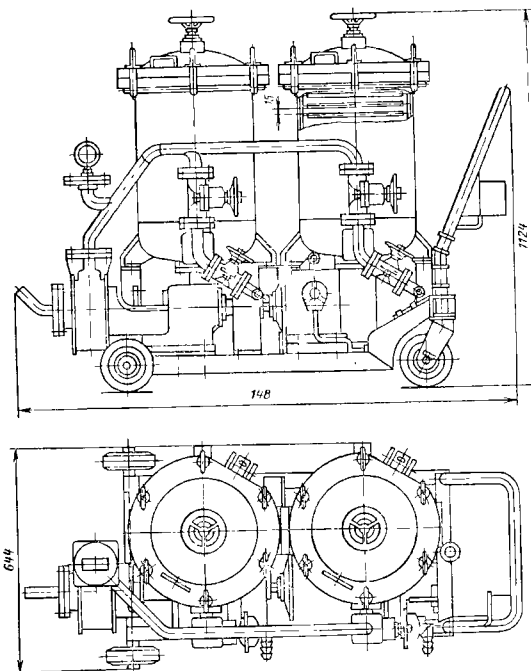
Фильтровальная установка модели 1×ДМ2-0,3Р с дисково-пакетными фильтрами
